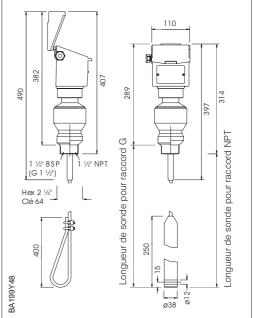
Dimensions : à gauche : FMP 232 à droite : FMP 332
